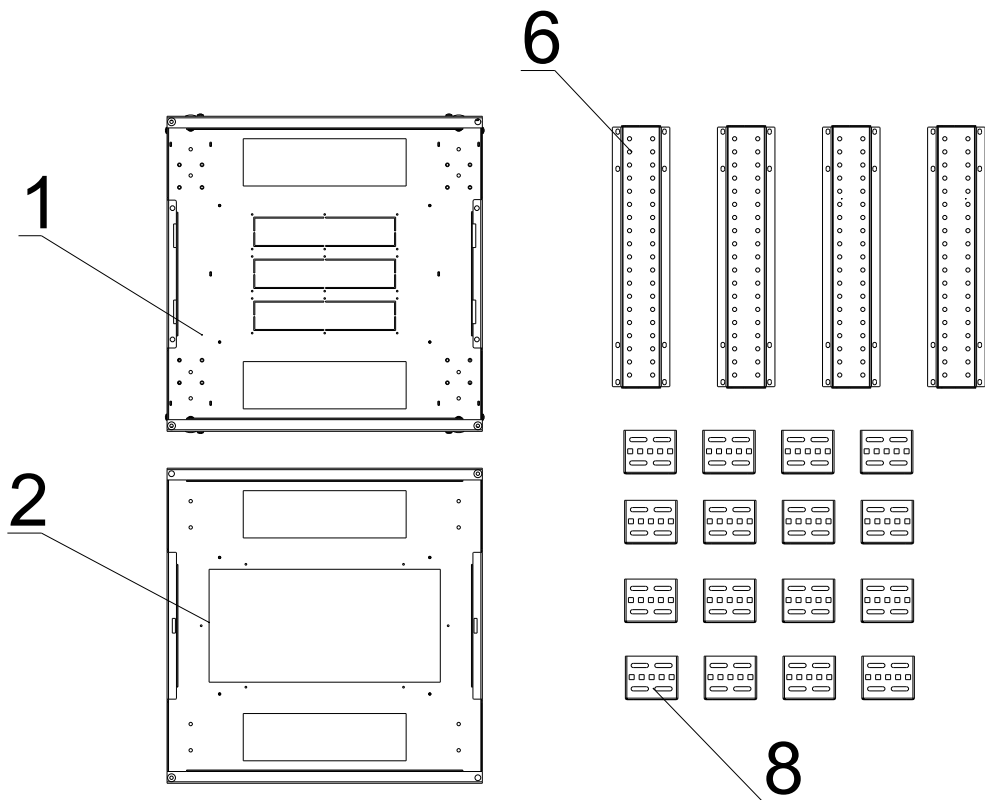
Коробка 1 комплектующие шкафа с обозначением на чертеже
